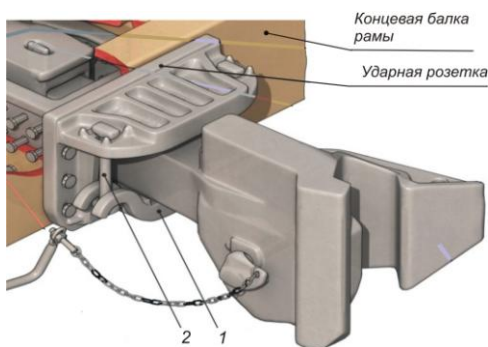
Общий вид центрирующего прибора жесткого типа для грузового вагона:
